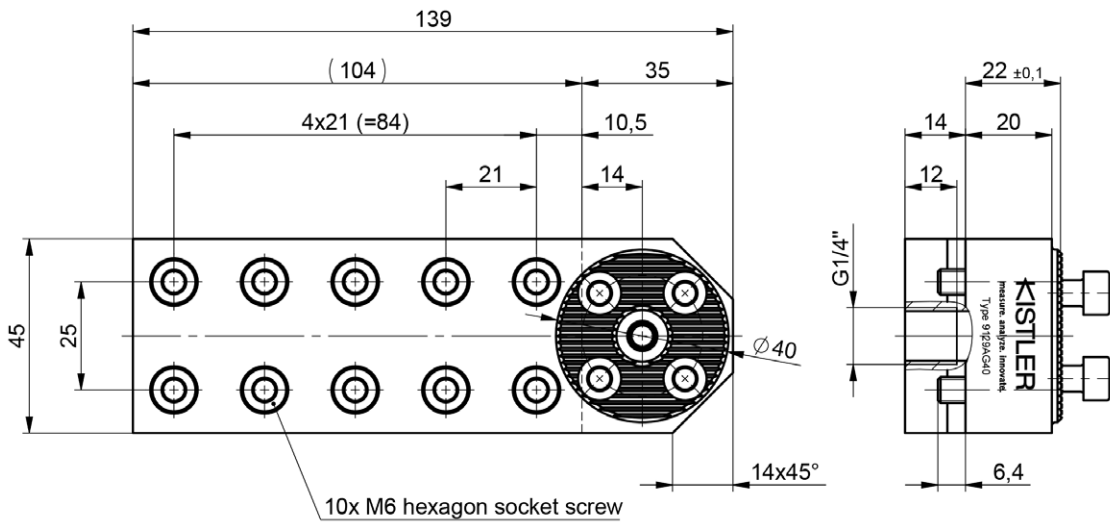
Werkzeughalter passend zu Sandvik Coroturn SL mit 40 mm Durchmesser, Typ 9129AG40
